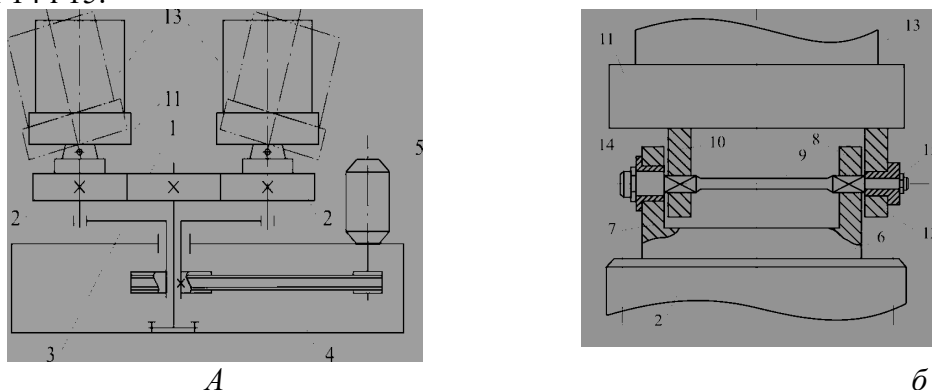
Багатокамерна відцентрово-вібраційна установка, а – загальний вигляд, б – механізм коливання
